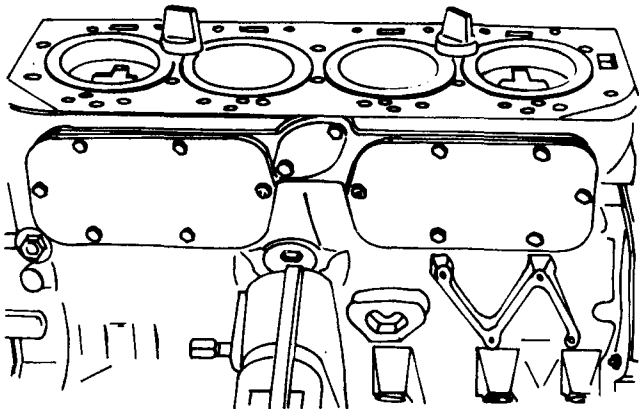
Крепление гильз цилиндров после демонтажа головки блока цилиндров.
